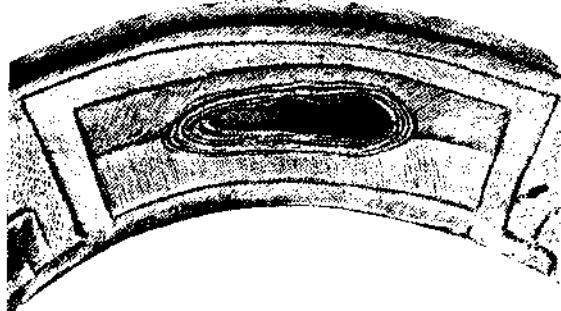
Подготовка к ремонту бортовой части покрышки.
